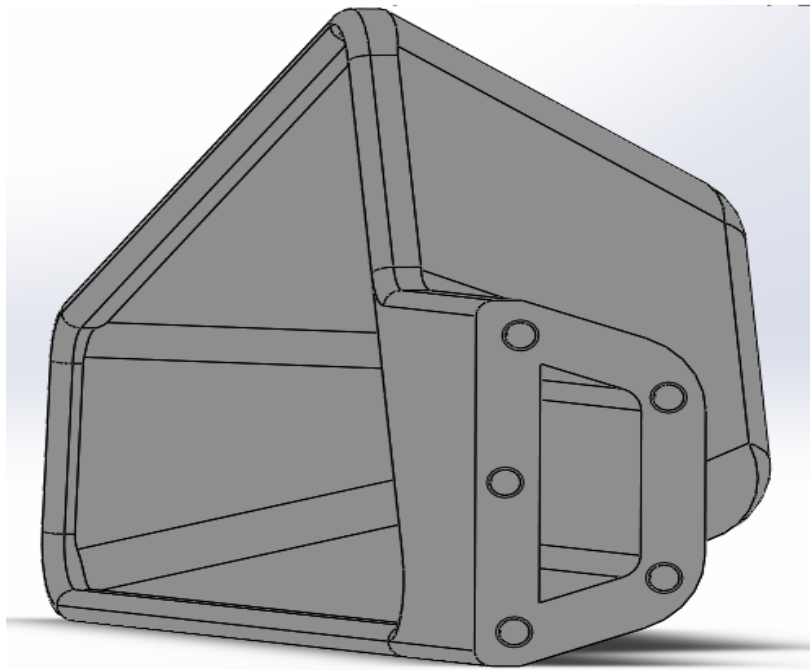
Disposición geométrica de los tornillos de anclaje.
